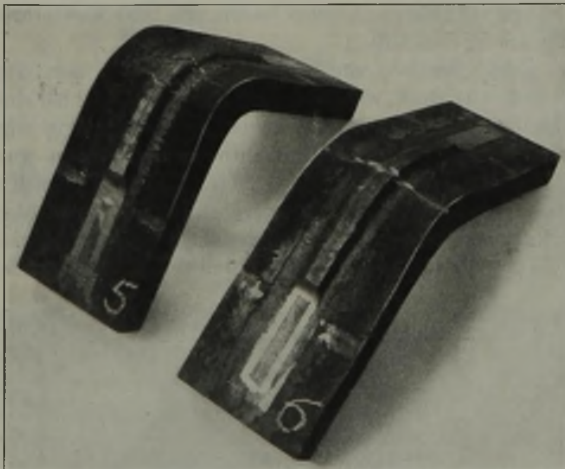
Biegeproben, bei denen ein Steg mit Kehlnähten aufgeschweißt und dann auf Kehlnahthöhe wieder abgehobelt wurde.
